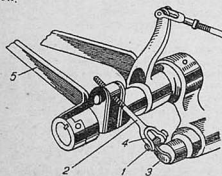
Привод механизма сцепления автомобиля ГАЗ-АА
